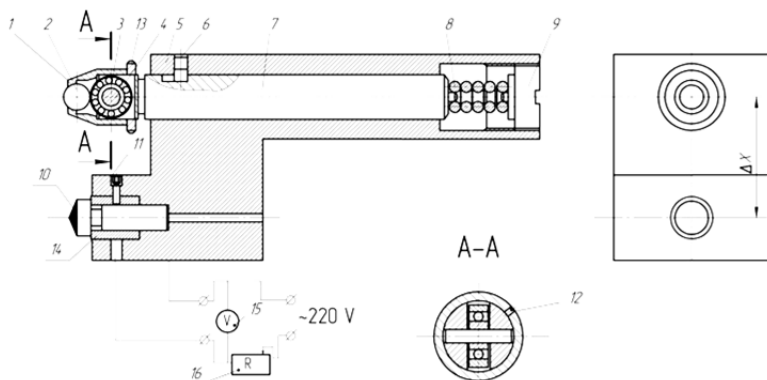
Комбинированный инструмент для отделочно-упрочняющей обработки:
